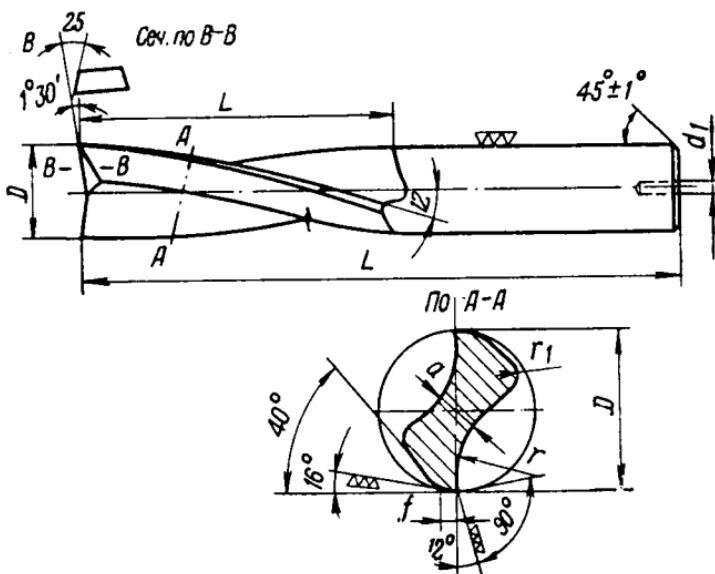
Конструкция концевых фрез с винтовым расположением режущих кромок
